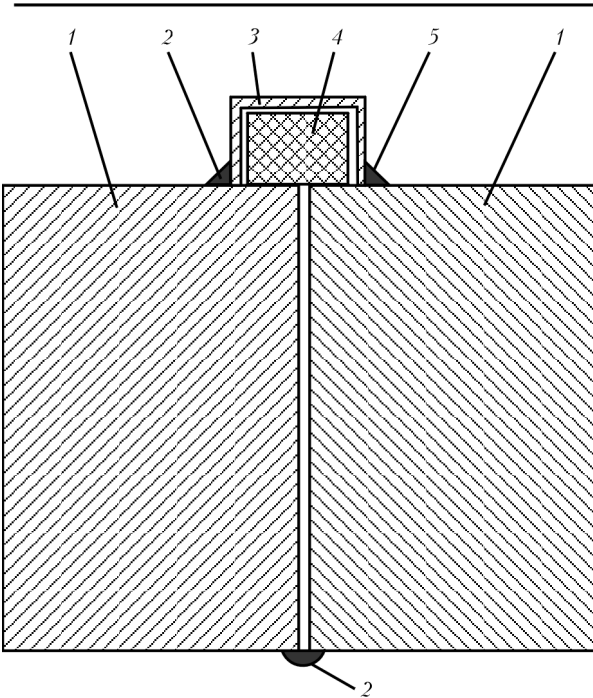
Схема АВП с широкими зазорами: 1 — основной металл; 2 — герметизирующие сварные швы; 3 — герметичный питатель; 4 — припой
